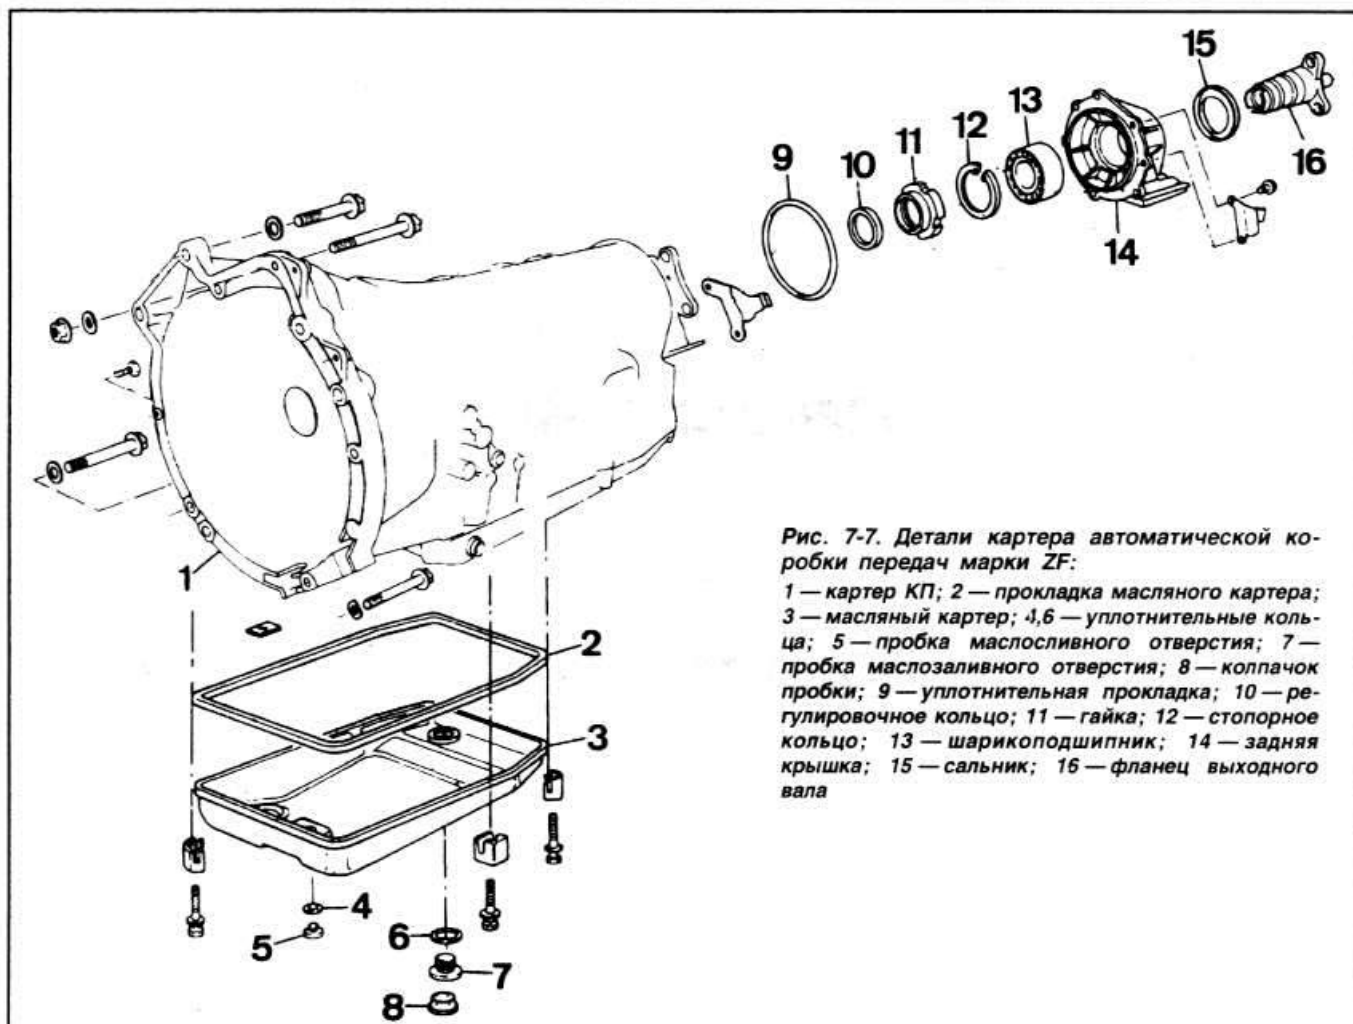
Детали картера автоматической коробки передач марки ZF:
